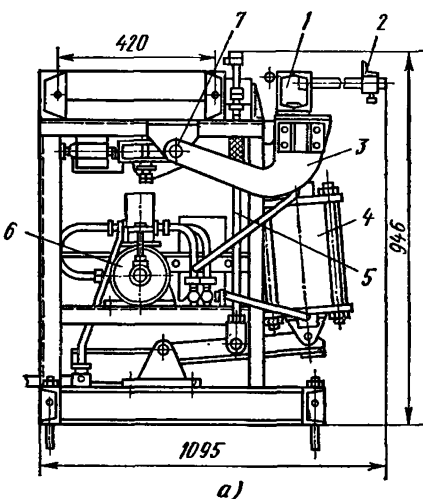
Станок СМЖ-353 для гибки сварных сеток:
